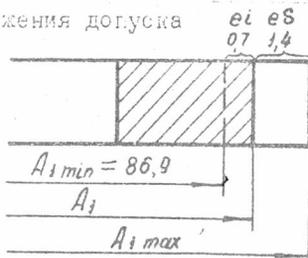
Схема расположения поля допуска на размер заготовки.
